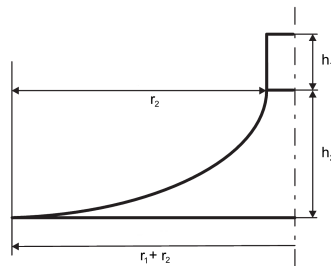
Sollgeometrie des Trichters mit Bemassung
